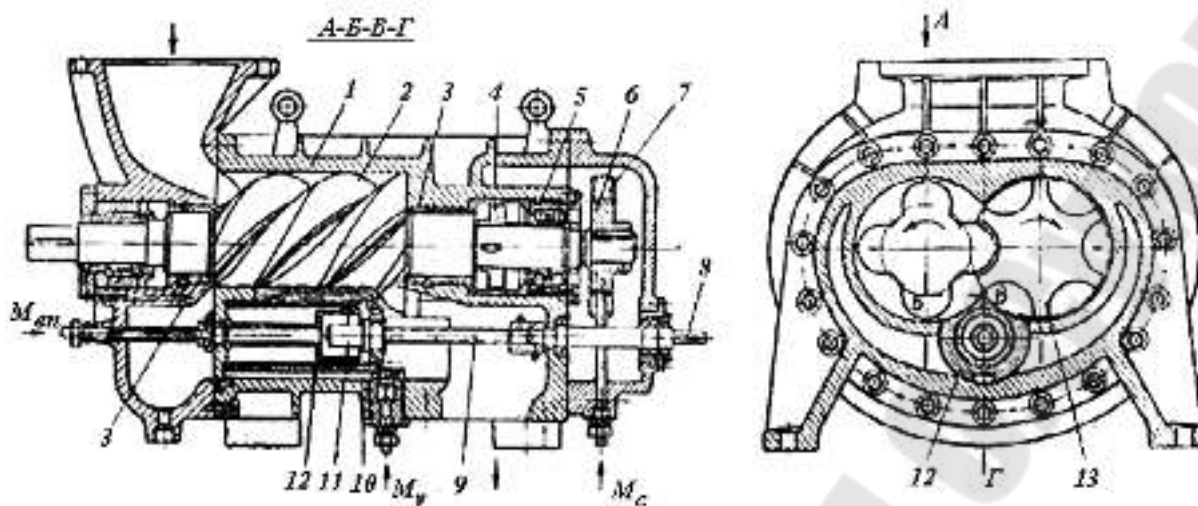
[13]. Маслозаполненный винтовой компрессор:
